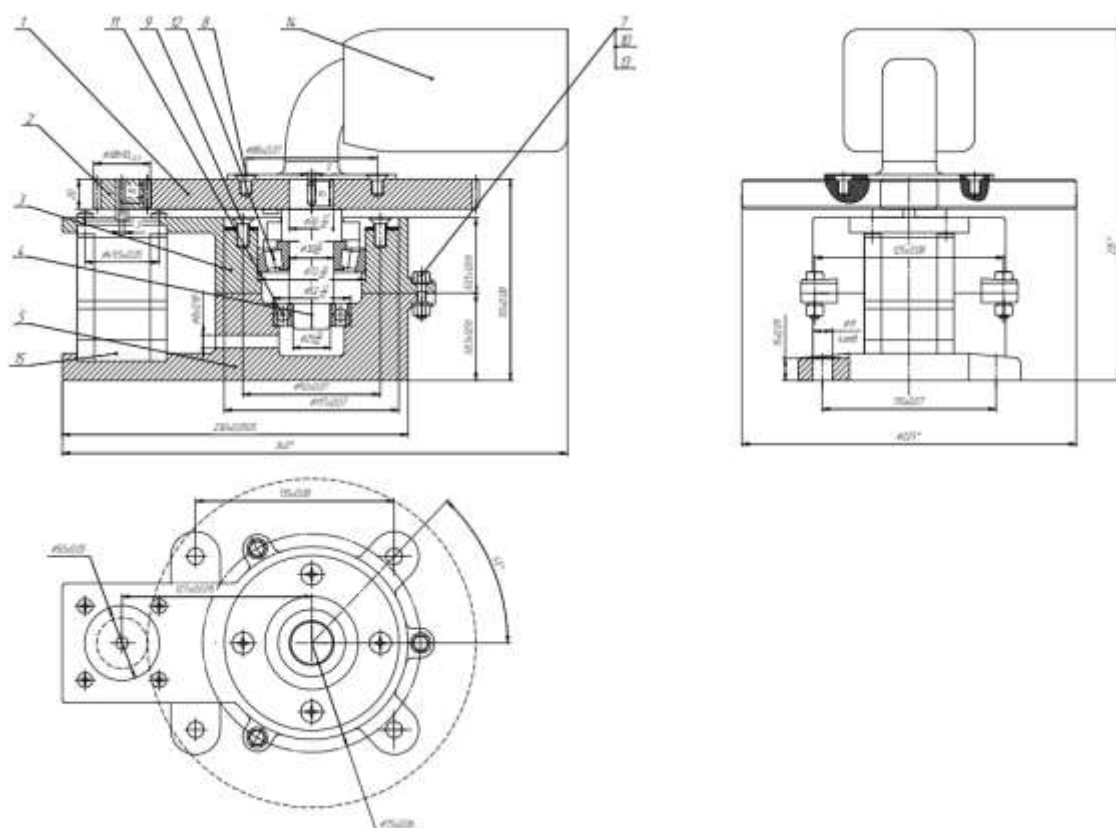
Головная часть робота. 1- зубчатое колесо, 2- шестерня, 3- корпус верхний, 4- вал, 5- корпус нижний, 6- крышка, 7- болт М6х50, 8- винт В2.М8-6gx14, 9- винт В2.М8-6gx20, 10- гайка М6-6Н, 11- подшипник 6205, 12- подшипник 7207, 13- шайба 6Л, 14- двухспектральная камера, 15- шаговый двигатель
